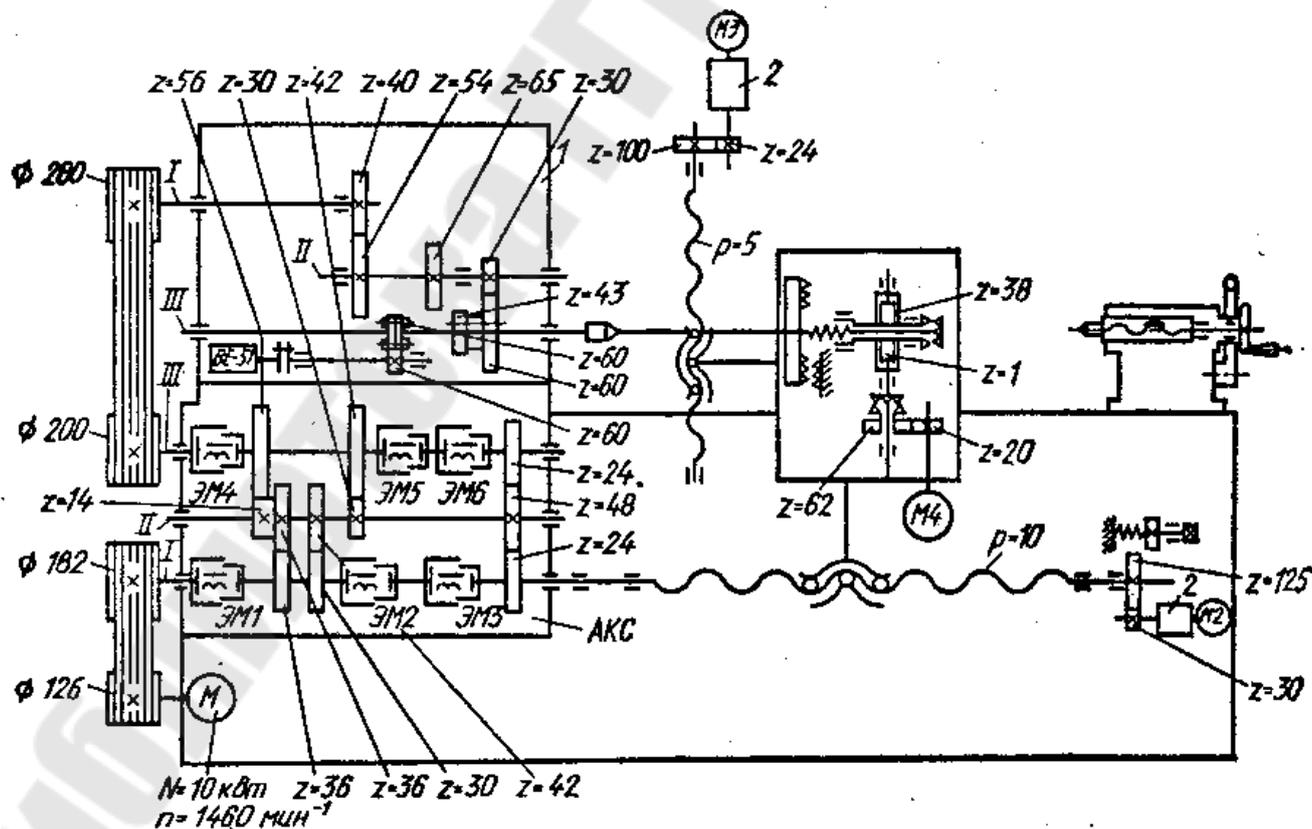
Кинематическая схема токарного станка с ЧПУ
